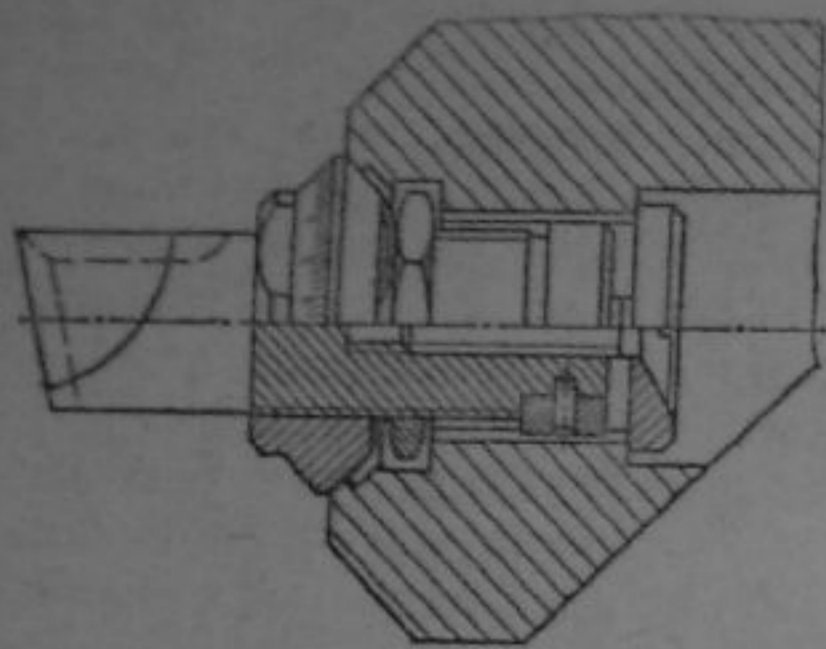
Резец-вставка с микрометрической регулировкой типа «Микробор»
